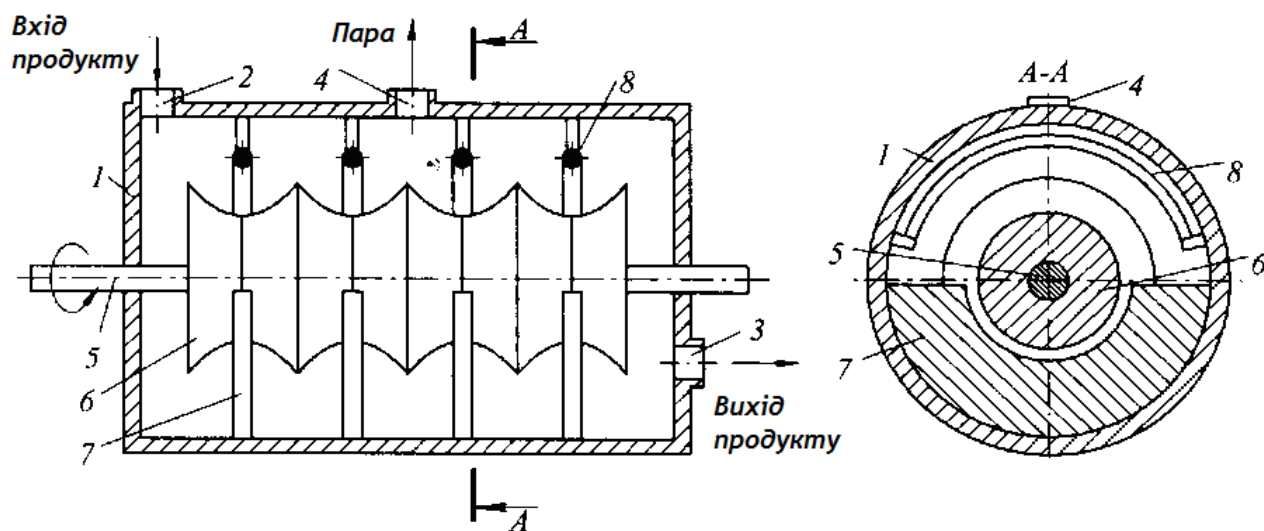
Пристрій для вакуумного концентрування рідин
